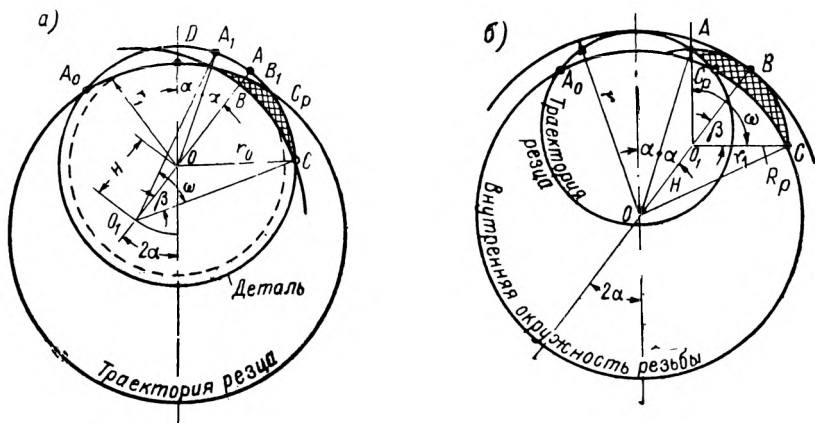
Схема контакта реза и детали при вихревом нарезании резьбы.
